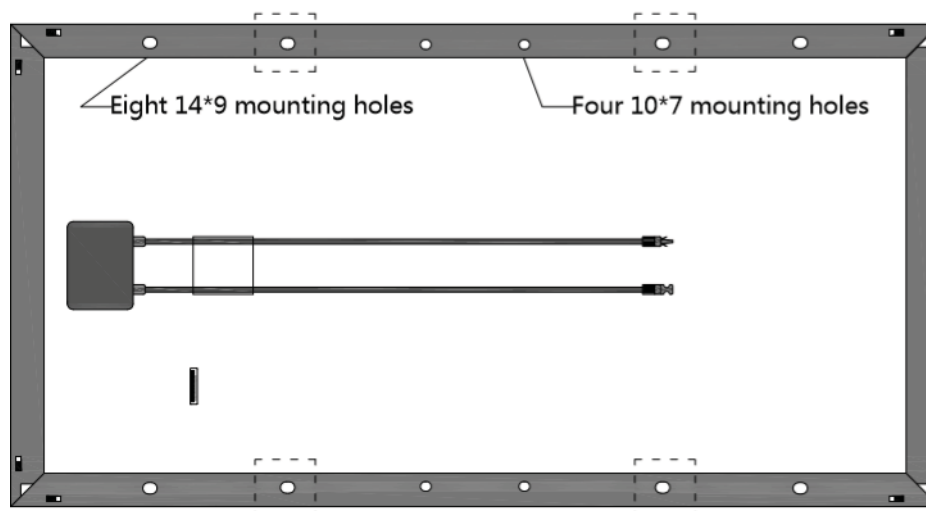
Módulo fotovoltaico instalado com método de fixação por parafuso (quatro orifícios de montagem)
